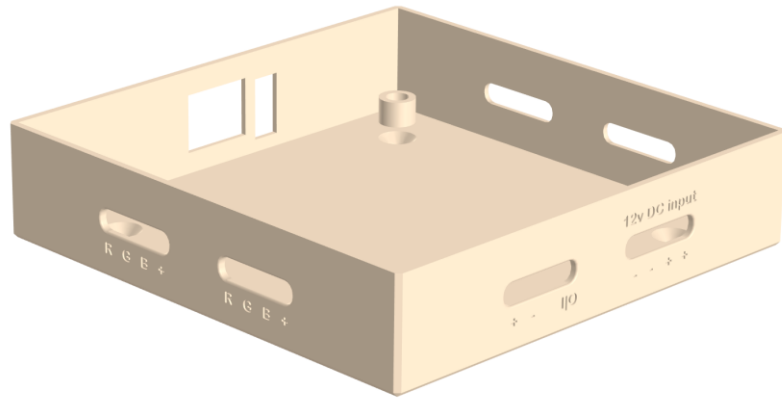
Нижня частина корпусу пристрою.
